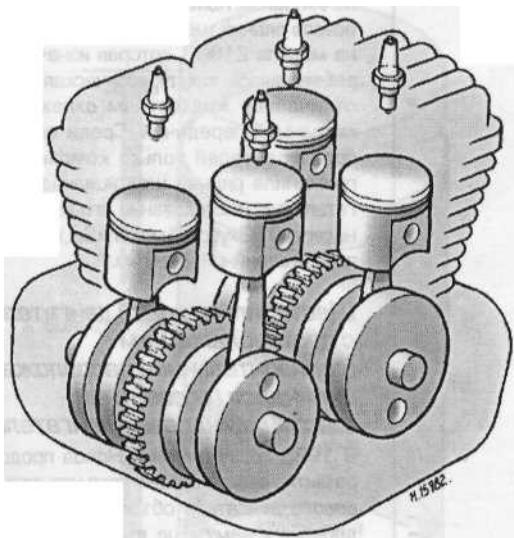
г Четырехцилиндровый двигатель с квадратным расположением цилиндров
